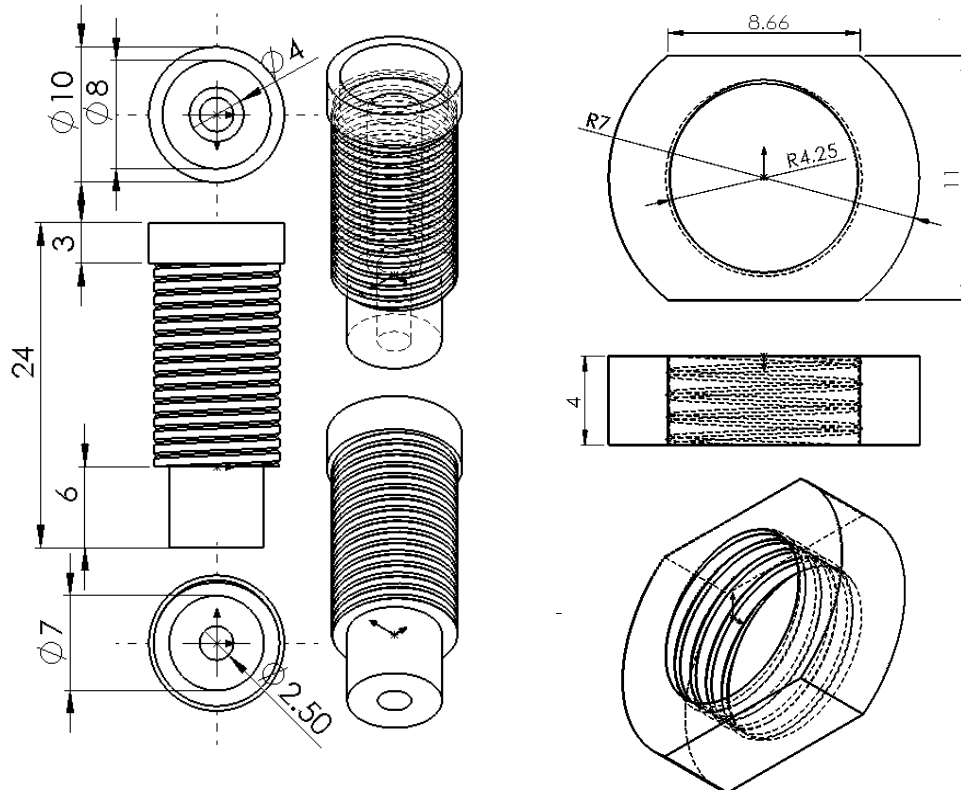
Dimensiones del tornillo y tuerca de acrílico porta electrodo superior.
